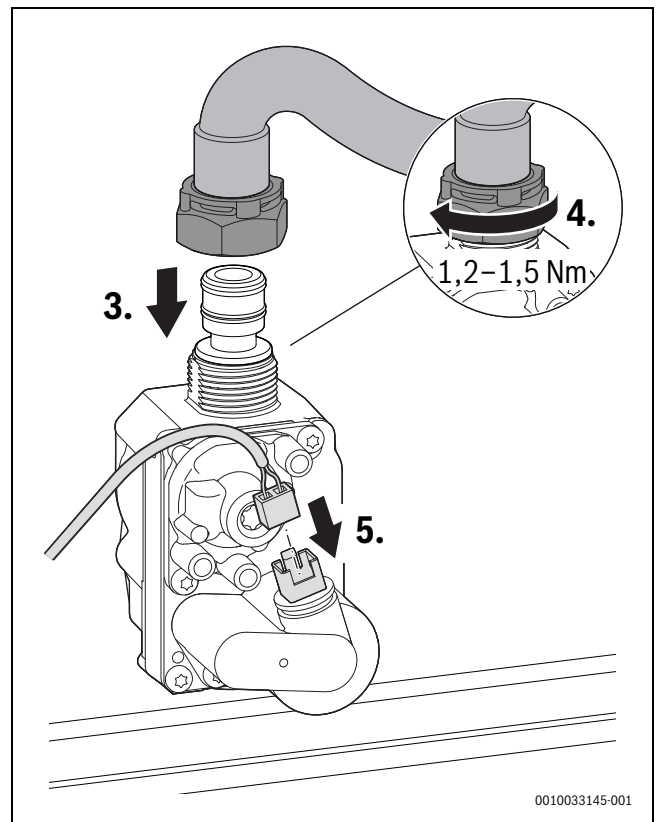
Gasschlauch und Stecker anschließen – Anzugsdrehmoment beachten
